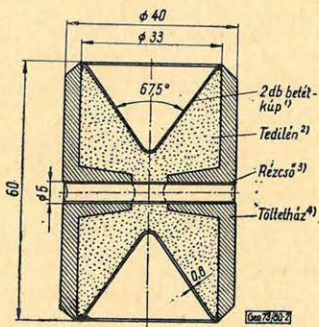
Perforator mit einer Tedilen-100 Ladung. (1, 2 Stück Einsatzkegel, 2, Tedilen, 3, Messingrohr, 4, Gehäuse)
